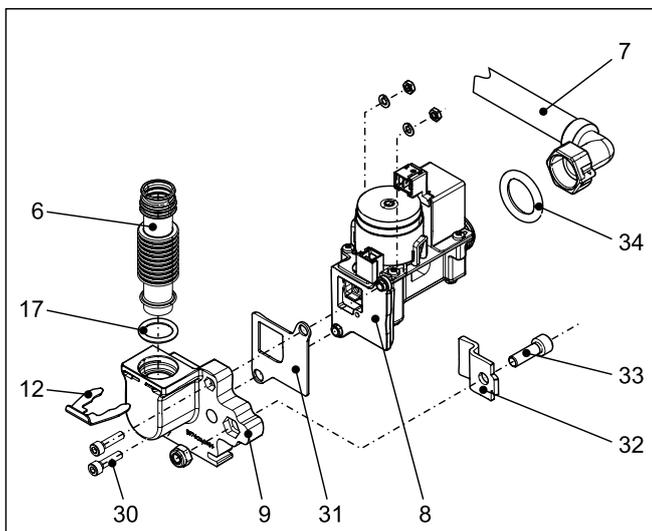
Bauteile der GCU compact Wärmecelle: Gasstrecke – Explosionsdarstellung (Legende siehe Tab. 7-1)
